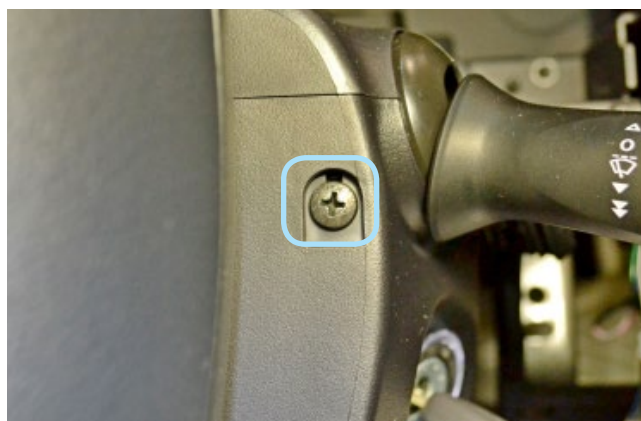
Саморезы крепления кожуха рулевого вала справа
